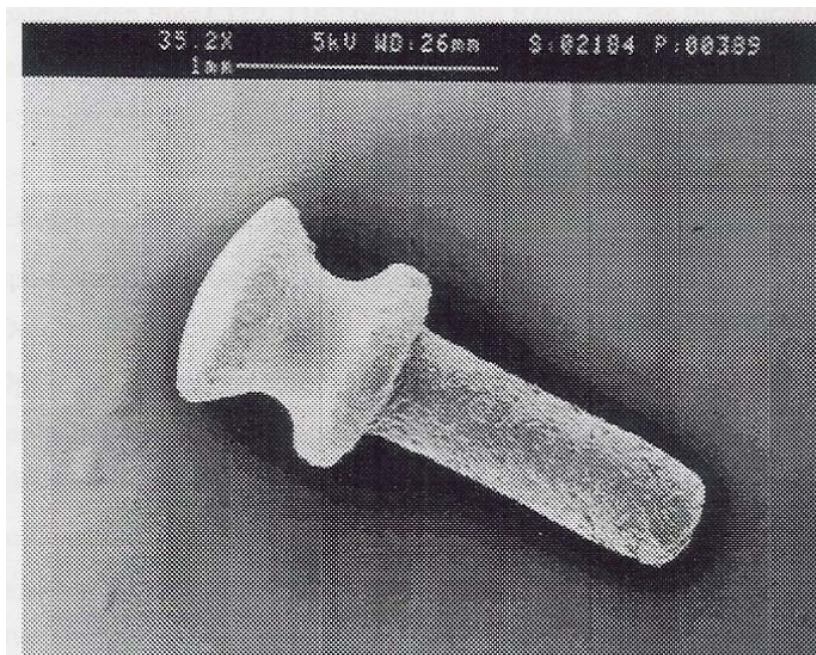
REM – Aufnahme des PCR – beschichteten Pins
